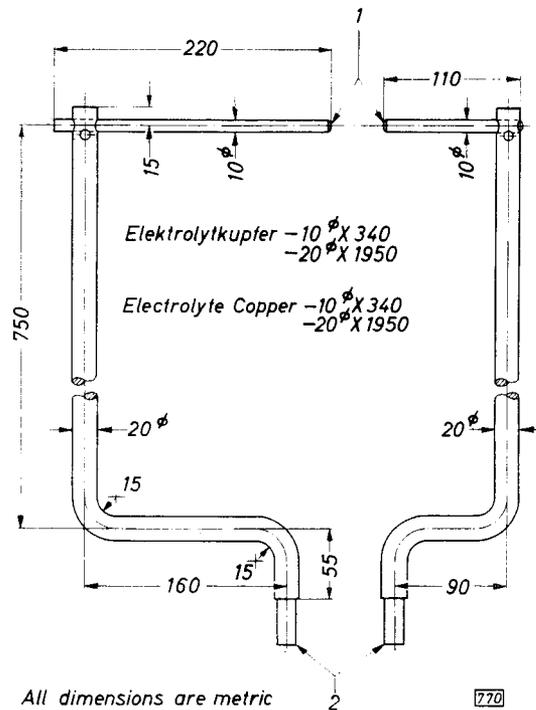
Maßskizze zur Selbstanfertigung der kompl. Schweißelektroden für das Zangenpunktschweißen der Vorderrahmenlängsträger an Bodenblech
